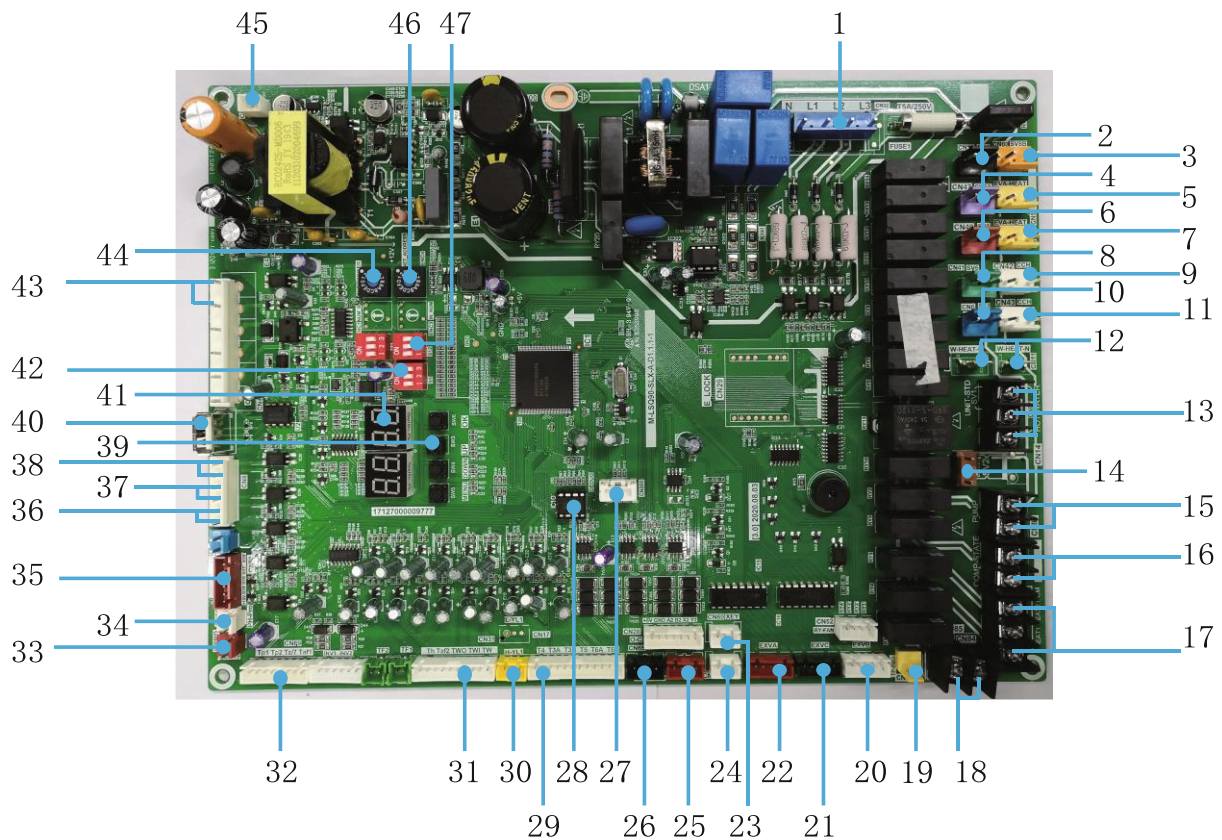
Placa principal de circuitos impresos del SCV-900EB y del SCV-1800EB
